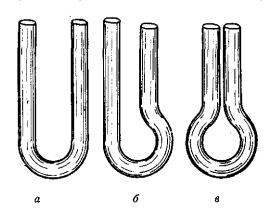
Кольцевой изгиб трубки: а — U-образный изгиб; б—изгиб одного колена; в —изгиб двух колен —готовое изделие-
